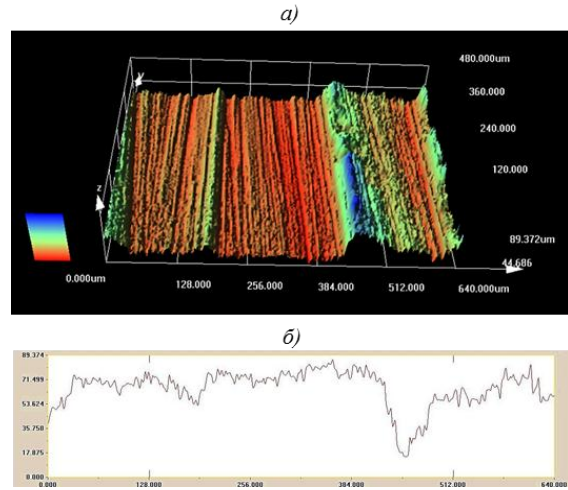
3D-изображение (а) и профиль участка поверхности (б) пластины Г6
